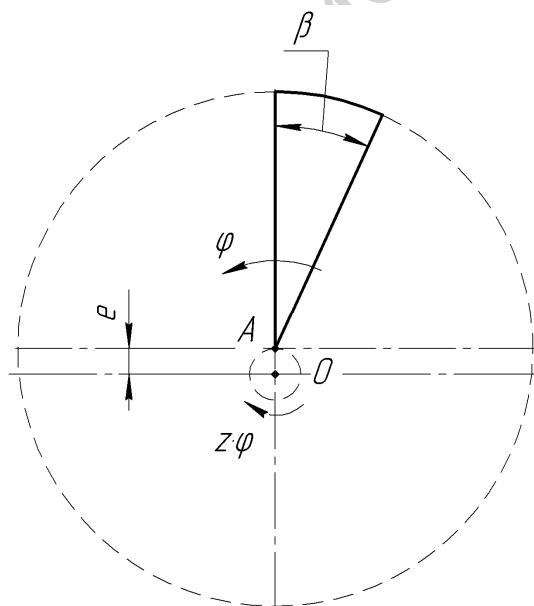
Схема для создания зубчатого колеса с эксцентриковой зубчатой поверхностью
